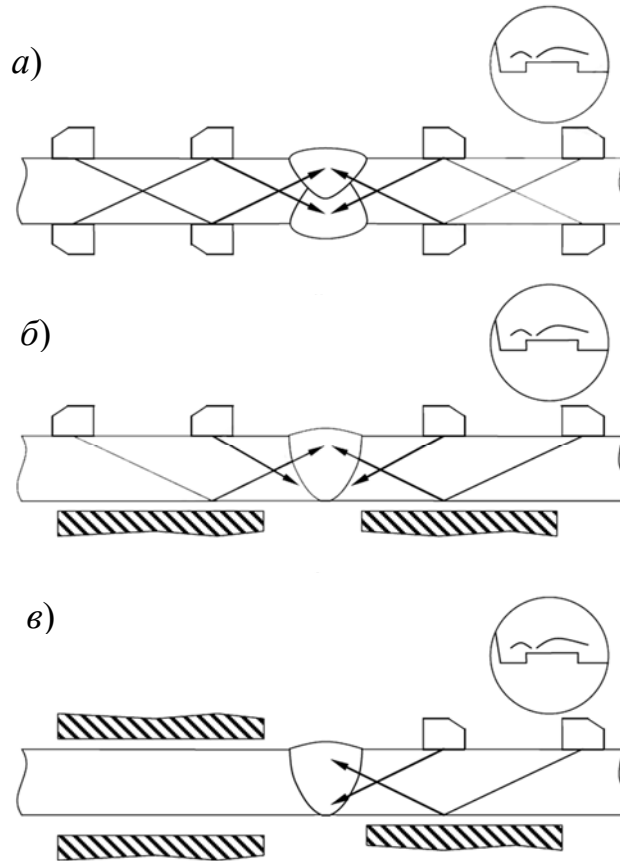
Схемы контроля стыковых сварных соединений
